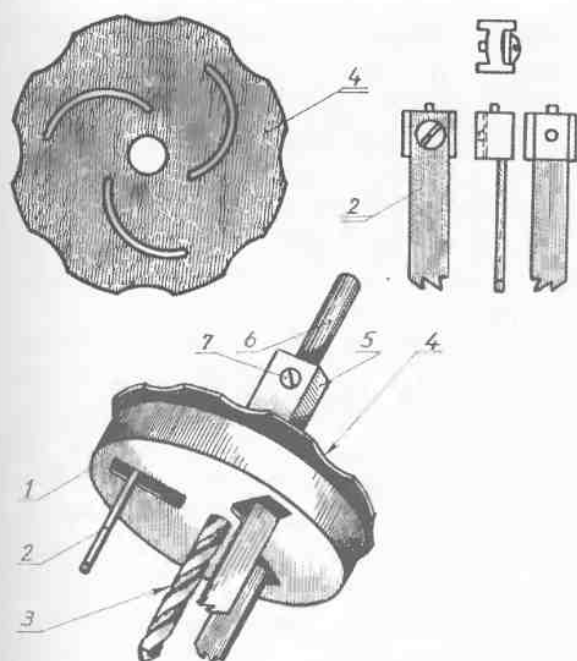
Кругорез «Сверлильная головка» заводского изготовления: 1 — корпус; 2 — чертеж резца; 3 — направляющее сверло; 4 — шайба — регулятор диаметра прореза; 5 — гайка для зажима шайбы; 6 — хвостовик сверла для зажима в патроне дрели; 7 — винт крепления сверла
